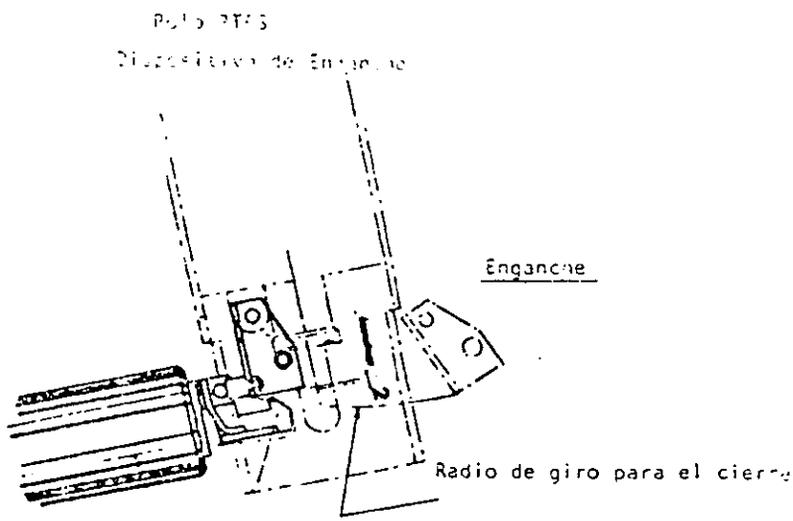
Polo RT6S. Dispositivo de Engranaje.
